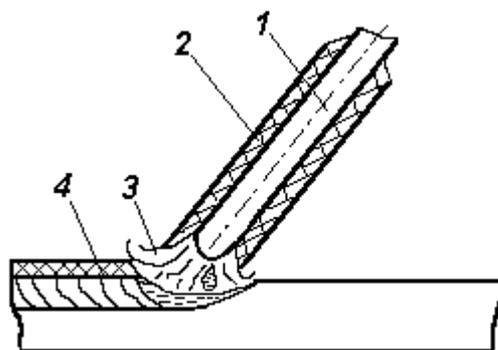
Схема процесса ручной дуговой сварки
